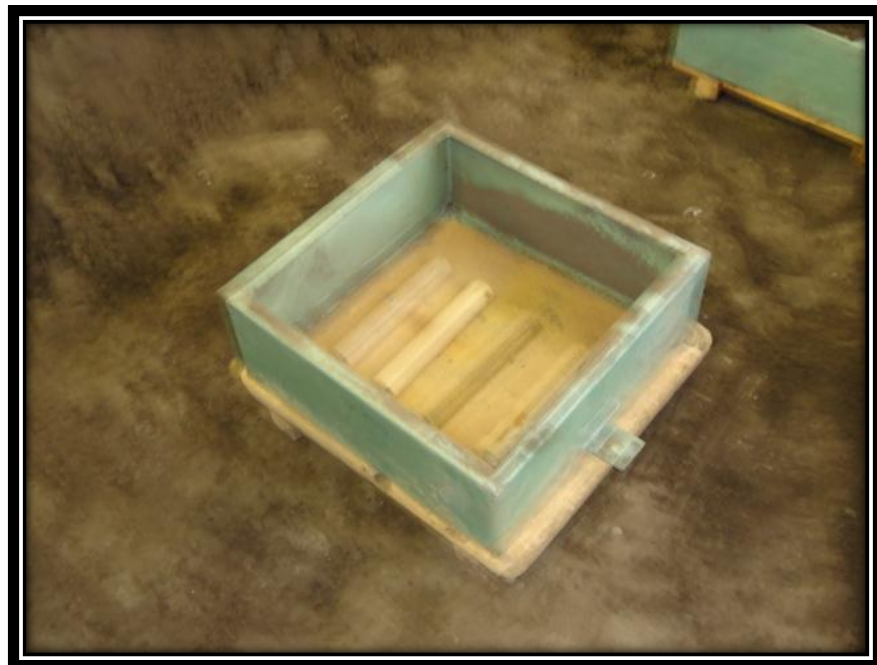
Disposición de los modelos de madera en la caja de moldeo. (Fuente: El autor)
